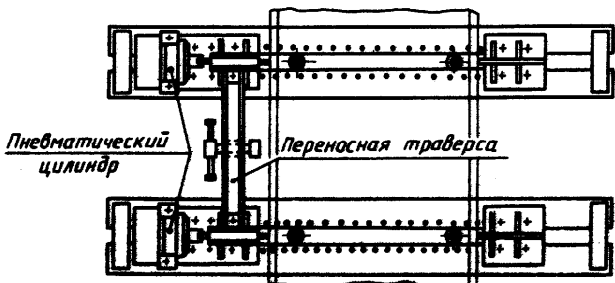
Универсальный сборочный кондуктор с пневматическими прижимами
